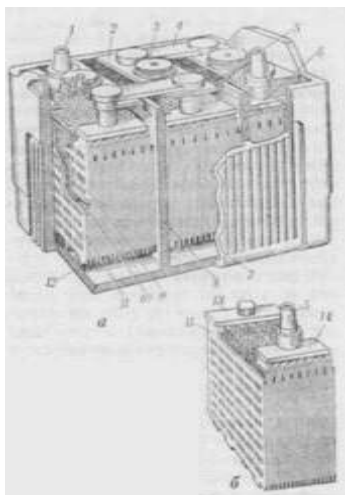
Акумуляторна батарея: а - 6 вольтова батарея; б – блок пластин; 1 і 5 – штирі; 2 – кришка; 3 – пробка; 4 –перемичка; 6 і 8 – перегородки; 7 – бак; 9 – позитивна пластина; 10 – сепаратор; 11 – негативна пластина; 12 – ребро; 13 і 14 – баретки.
